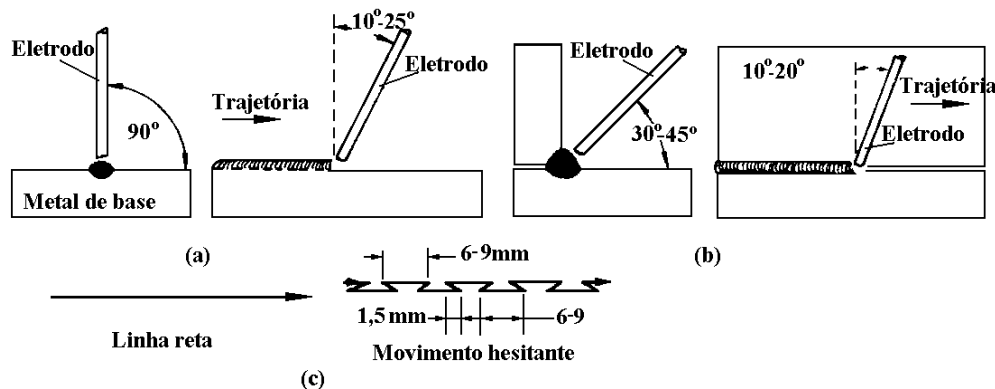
Técnicas de soldagem SMAW na posição plana, a) Eletrodo reto, b) Eletrodo inclinado
